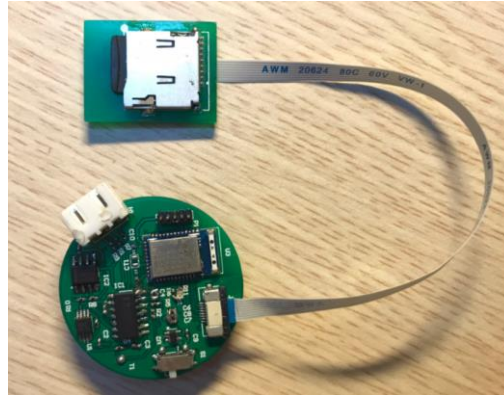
PCB mặt top mạch đo tín hiệu EMG
